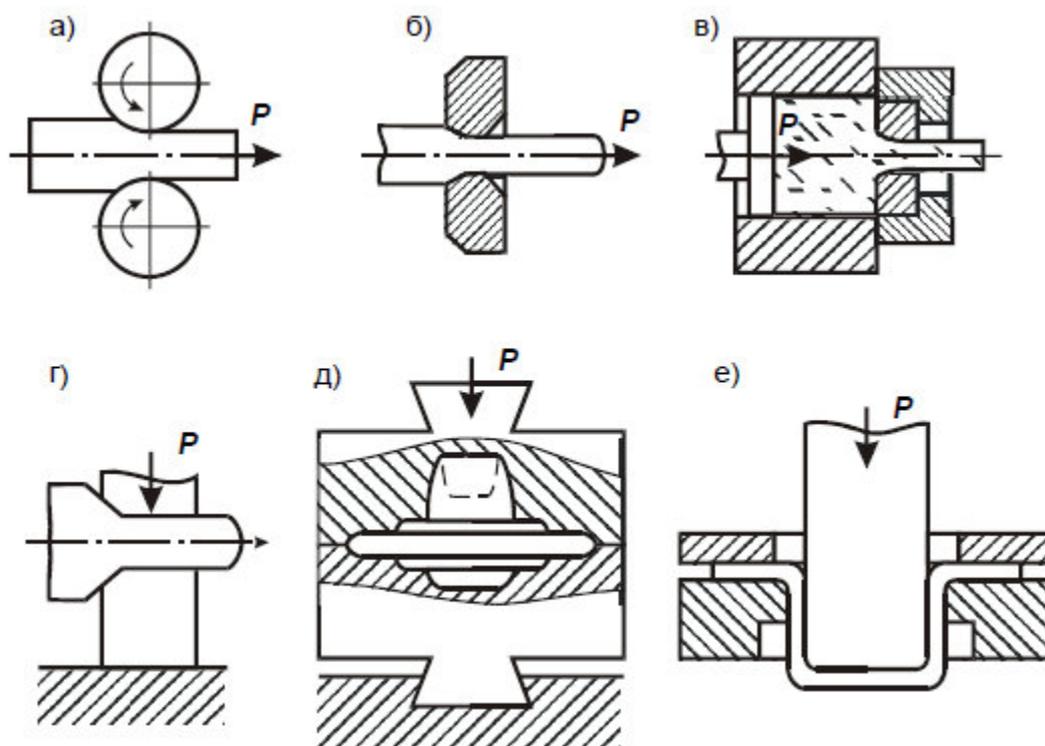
Принципиальные схемы основных способов обработки давлением: а - прокатка; б - волочение; в - прессование; г - ковка; д - объемная штамповка, е – листовая штамповка
